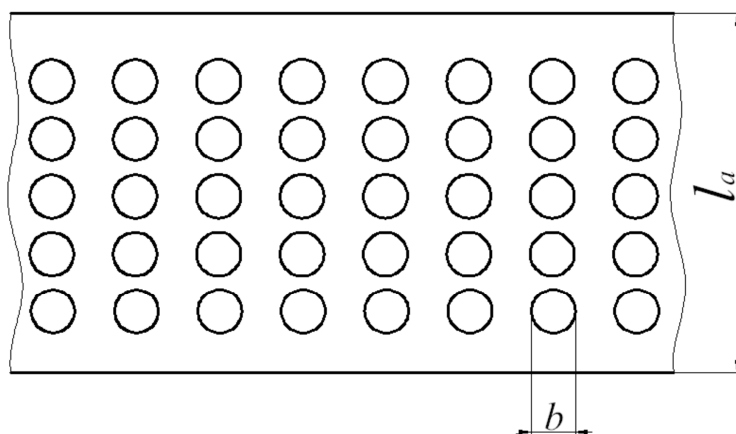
Развертка поверхности ПФР со сквозными отверстиями
